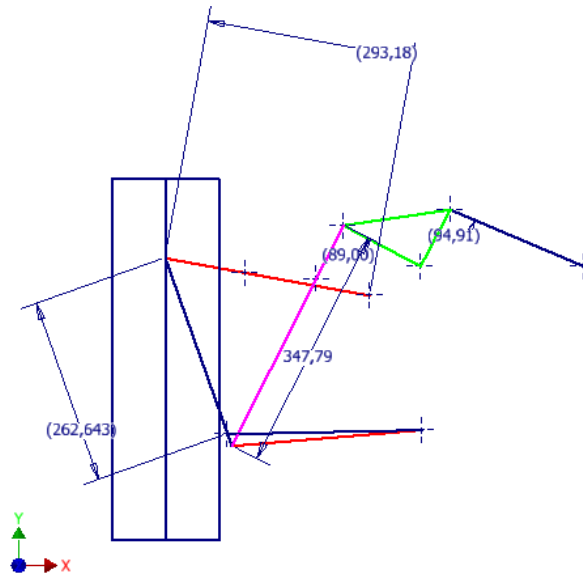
Proyección en un mismo Plano de la Geometría de la Suspensión Eje Trasero
